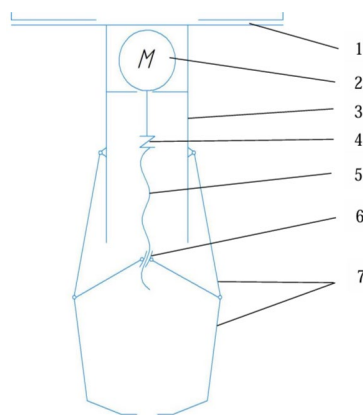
Кинематическая схема ЗУ квадрокоптера: 1 — крепление к квадрокоптеру; 2 — мотор; 3 — корпус; 4 — муфта; 5 — винт; 6 — гайка; 7 — рычаги
